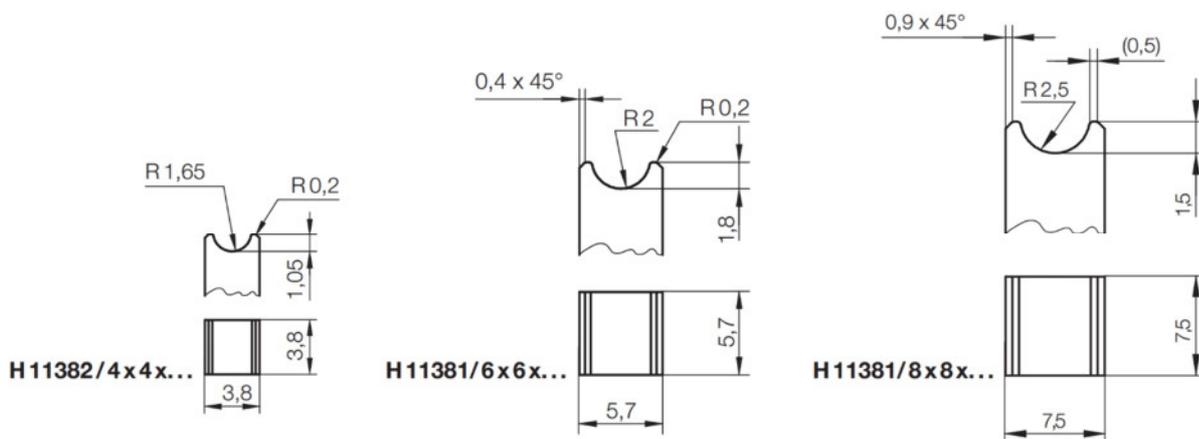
Herramienta de montaje para elementos calefactores tubulares
